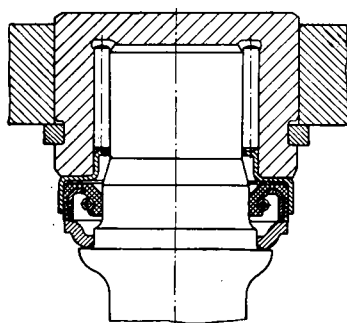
Подшипник конструкции ГАЗ для автомобиля ГАЗ-24
